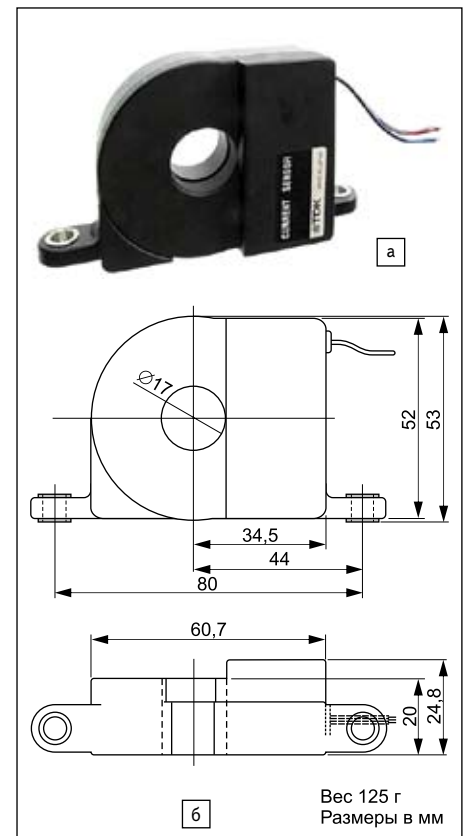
а) Внешний вид датчика; б) форма и размеры
